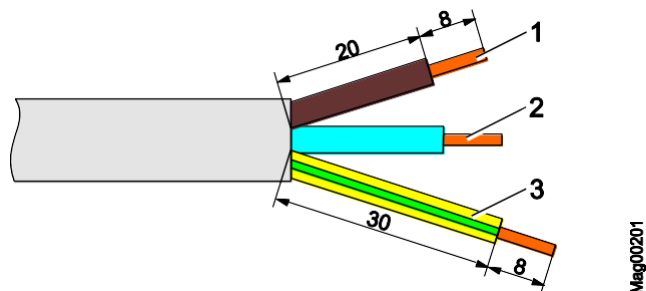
Aislar el cableado de red eléctrica (dimensiones en mm)
